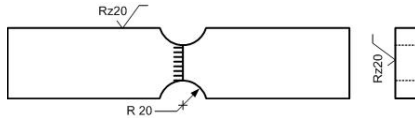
Образец для определения временного сопротивления металла шва при испытаниях на статическое растяжение.
